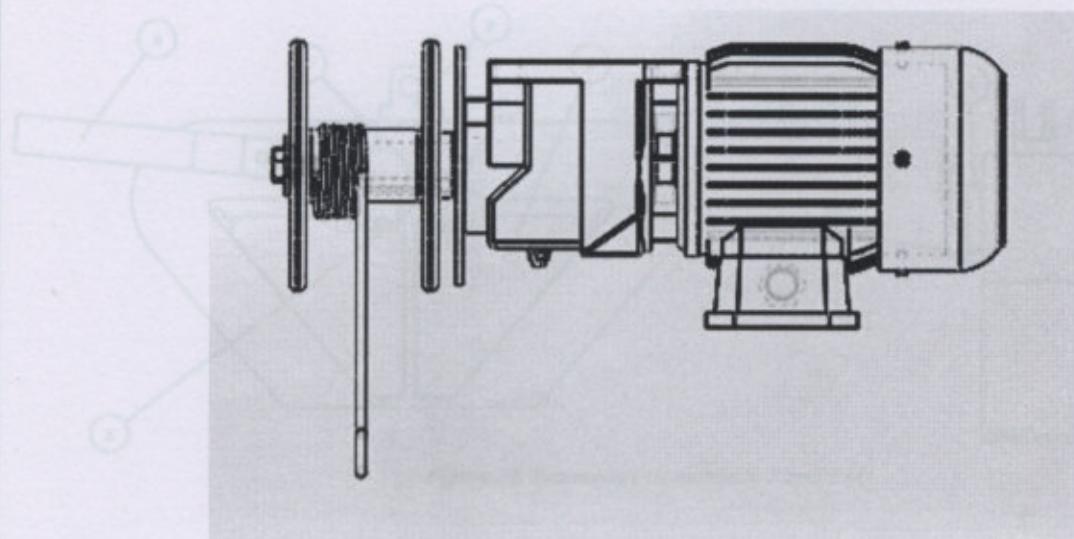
Aparejo eléctrico. Ver detalles en anexo.
